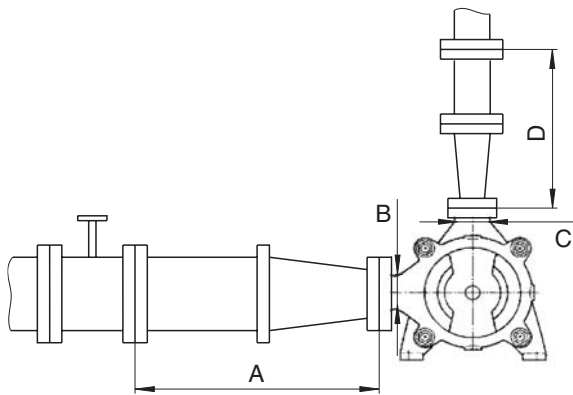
Gerade Rohrleitungslängen vor und nach der Pumpe (empfohlen)
